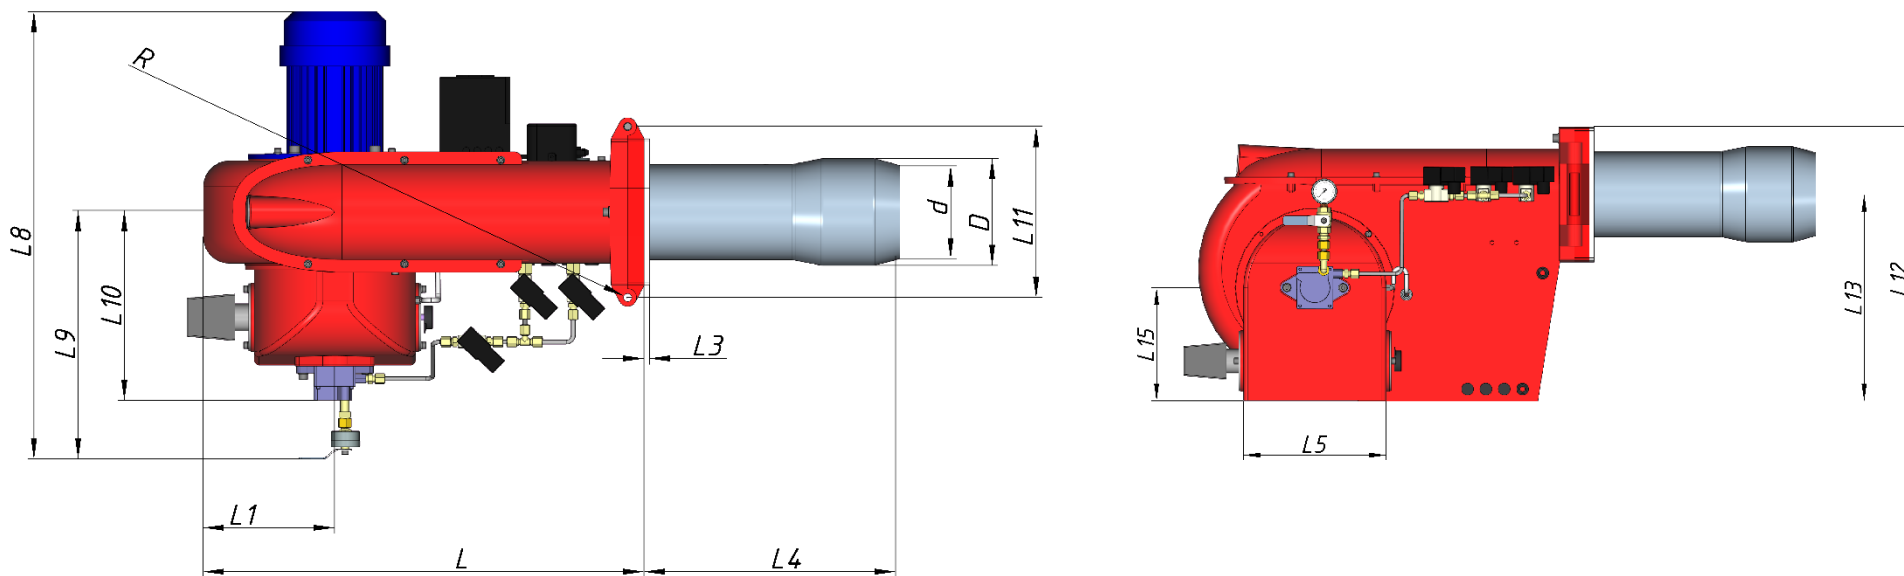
Габаритные и присоединительные размеры горелок ГДБ-0,63...ГДБ-10,9
